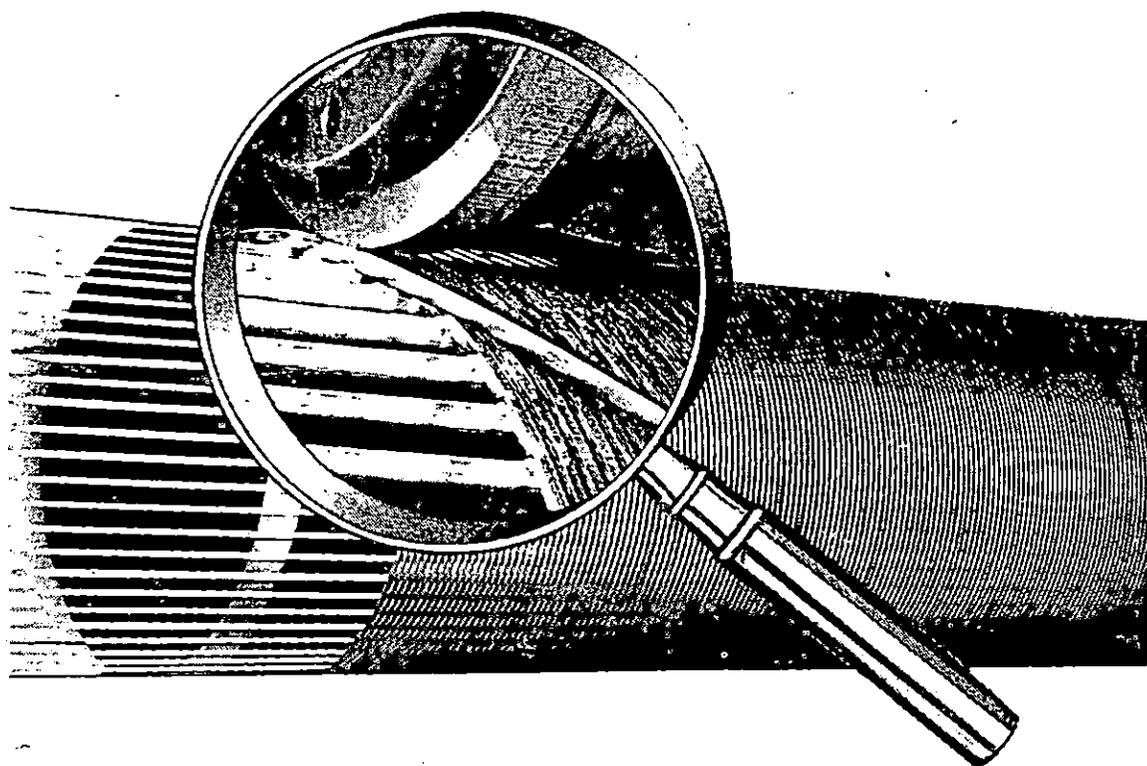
Fabricación de la rejilla Johnson de ranura continua y soldadura global, para pozos. La rejilla puede fabricarse de cualquier metal o aleación que sea resistente a la soldadura.
